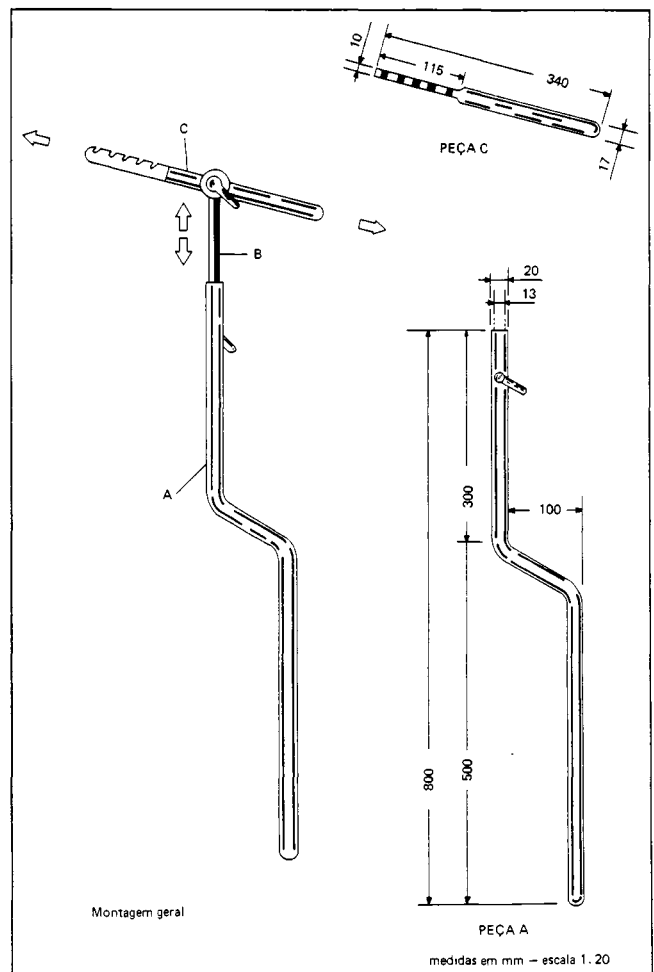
Esquema geral do suporte-posicionador e destaque das peças A e C.
